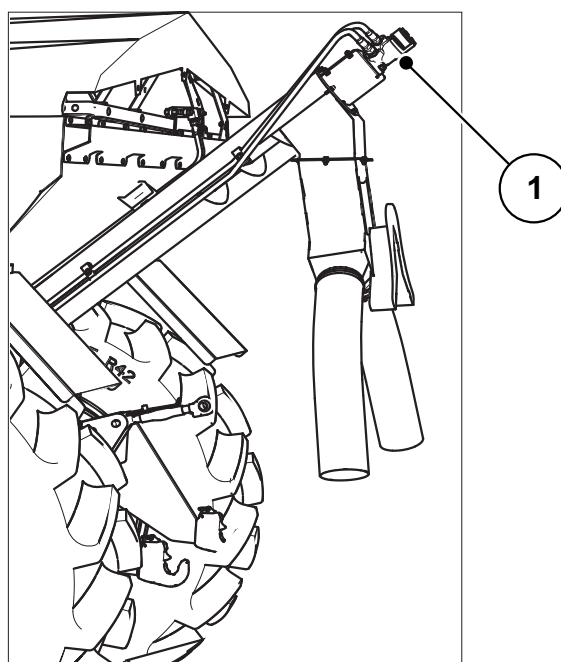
Siłownik hydrauliczny plandeki – przód
